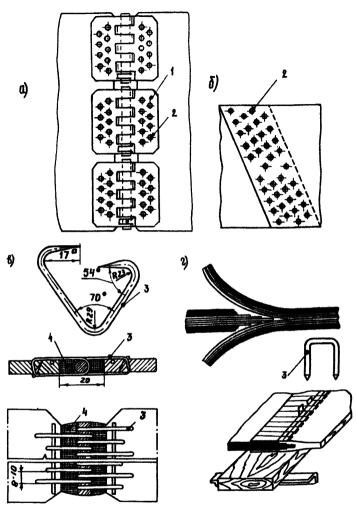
Стыковка лент механическими средствами: а — шариграми; б — заклепками; в — крючкообразными скоба ми с тросом; г — П-образными скобами; І — петли; 2 — заклепки; 3 — скобы; 4 — уплотнительный шнур
